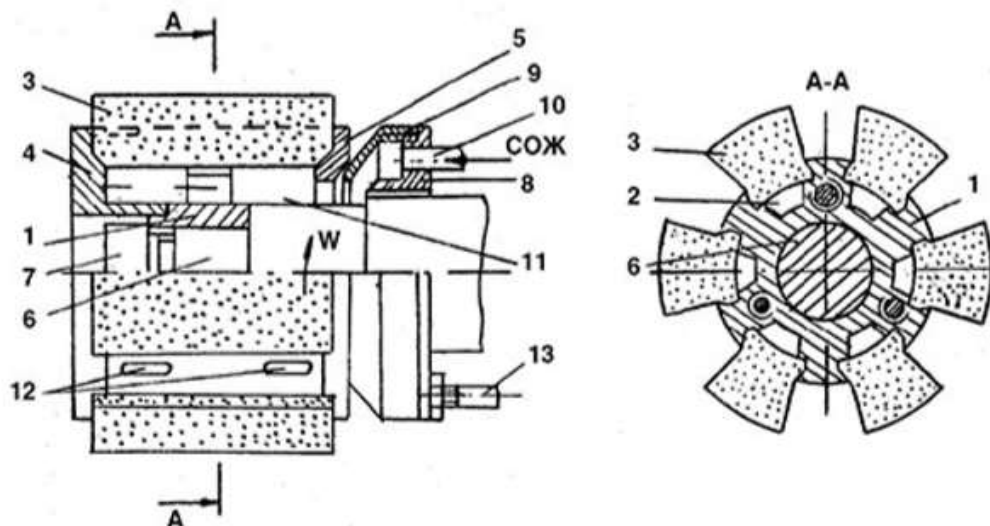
Конструкція зірного абразивного круга з переривчастою ріжучою поверхнею і пристроєм для подачі МОР: 1 - корпус; 2 - паз корпусу; 3 - абразивний сегмент; 4, 5 - кришки; 6 - шпиндель; 7 - болт; 8 - фланець; 9 - конічна гайка; 10 - трубопровід; 11 - порожнина інструменту; 12 - поздовжні щілини; 13 - стрижень.
